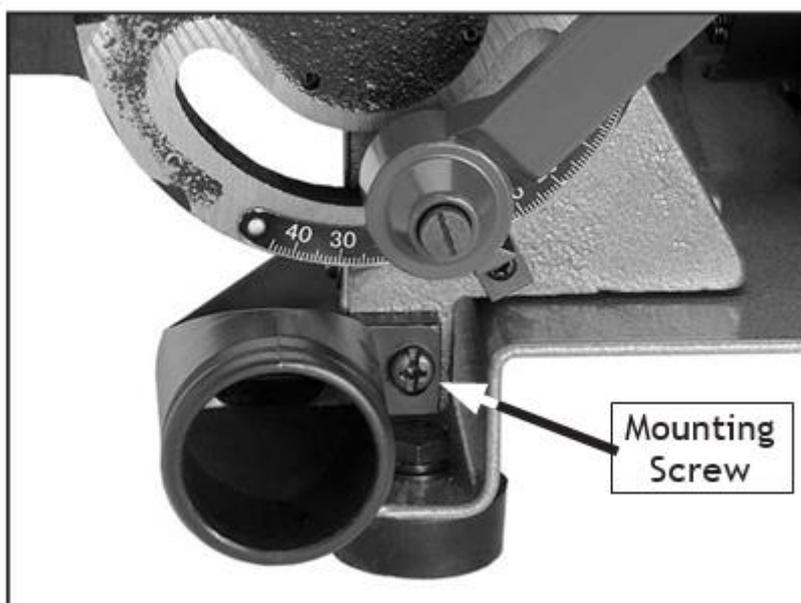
Установка патрубка аспирации пыли для узла шлифовального диска .
